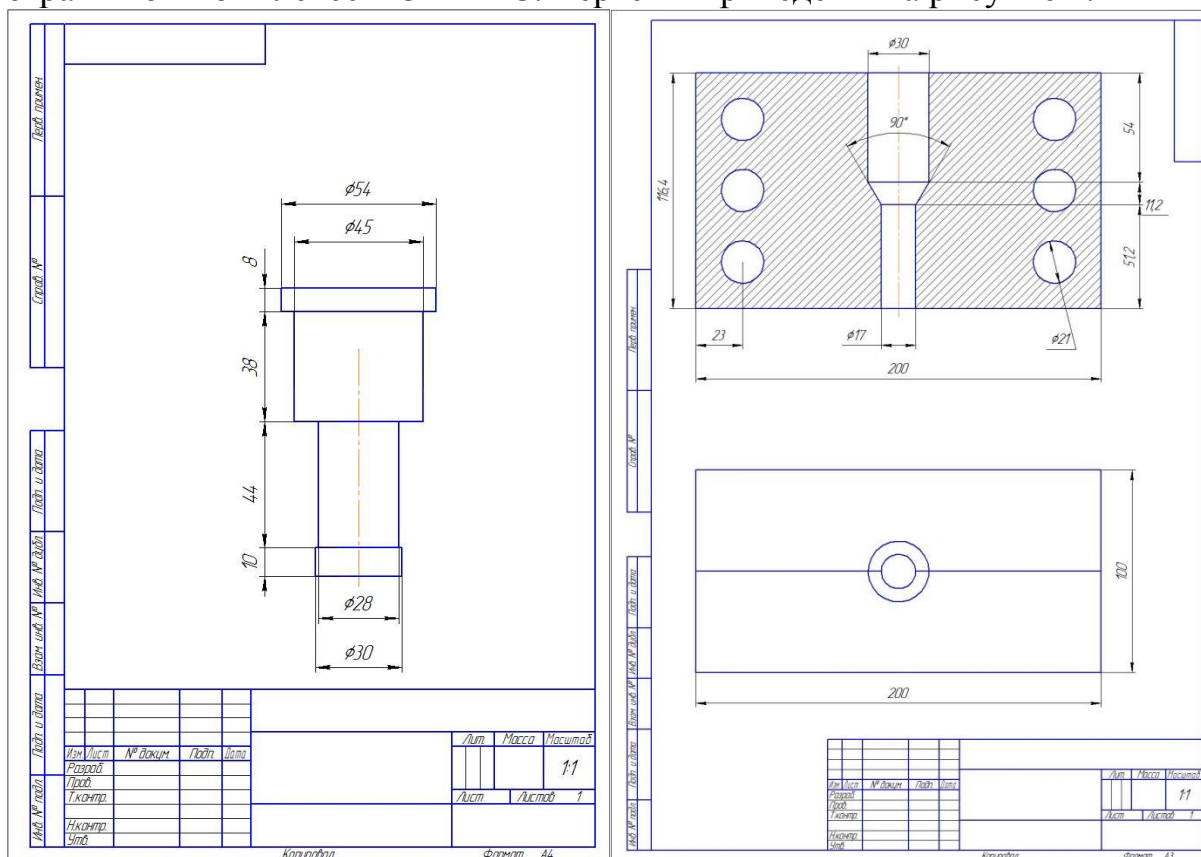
Рабочие чертежи штампа для выдавливания
